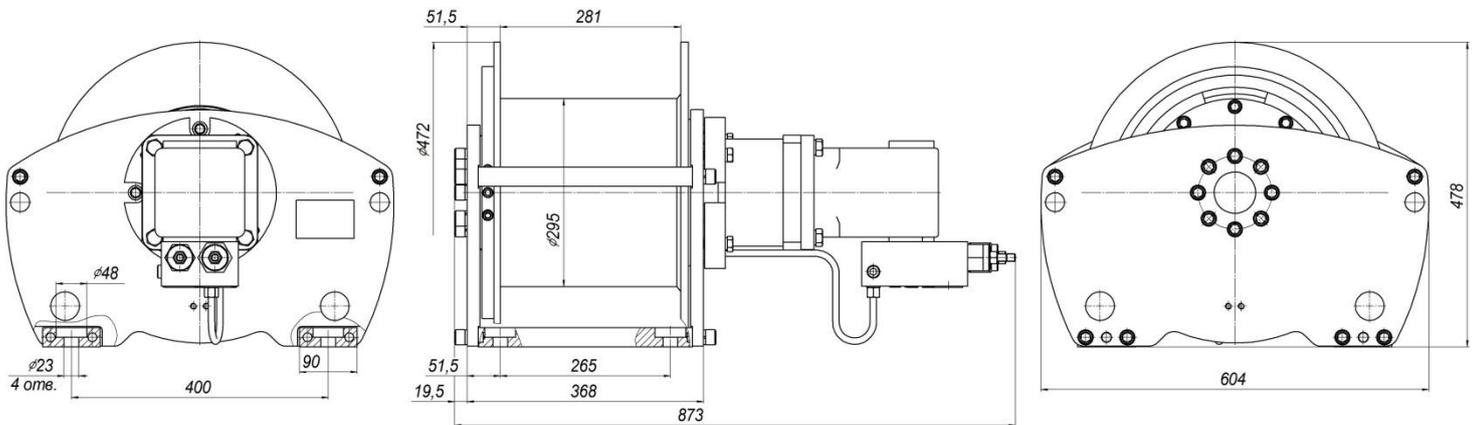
Общий вид, габаритные и присоединительные размеры
